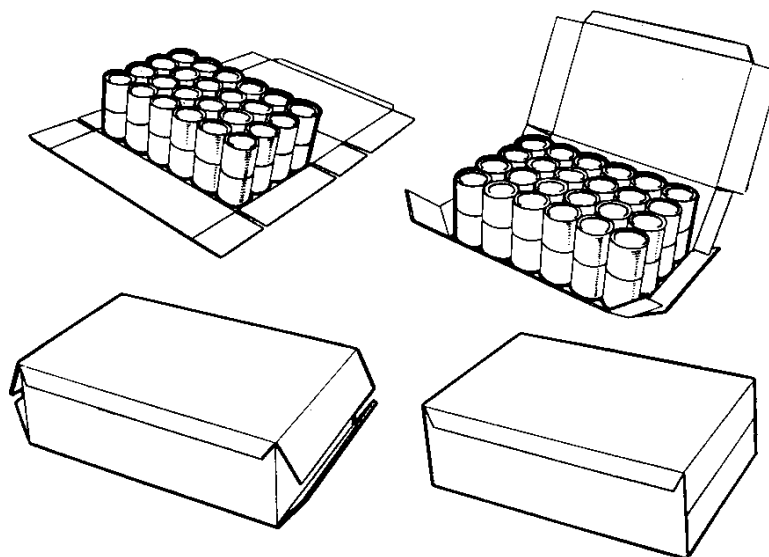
Пакування консервних банок способом обертання заготовки навколо пакета виробів
